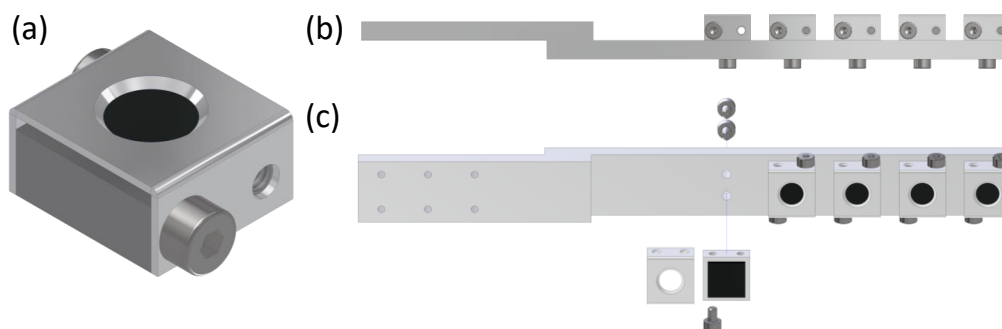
(a) Zeichnung des einzelnen Probenblocks; (b) Seiten- und (c) Draufsicht des gesamten Probenhalters. Die Probenblöcke sind mit Schrauben auf den Probenhalter geschraubt. Dies erlaubt die wiederholbare Positionierung zum Beispiel bei der Messung vor und nach der Bestrahlung mittels SHI.
